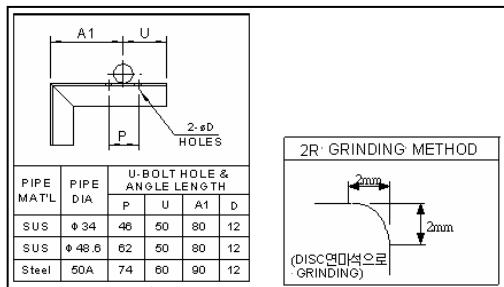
Bolt Hole Pitch 및 크기 표기와 Grinding Symbol 표기
